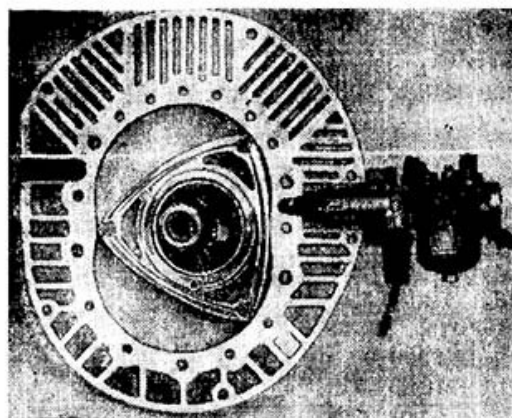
Двигатель КМ-37 фирмы Фихтель и Закс
